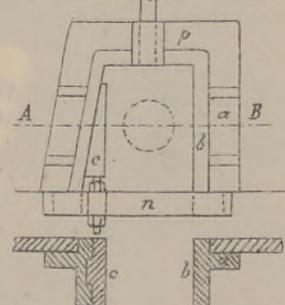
Guias da caixa de lubrificação. Alçado e corte horizontal segundo AB
